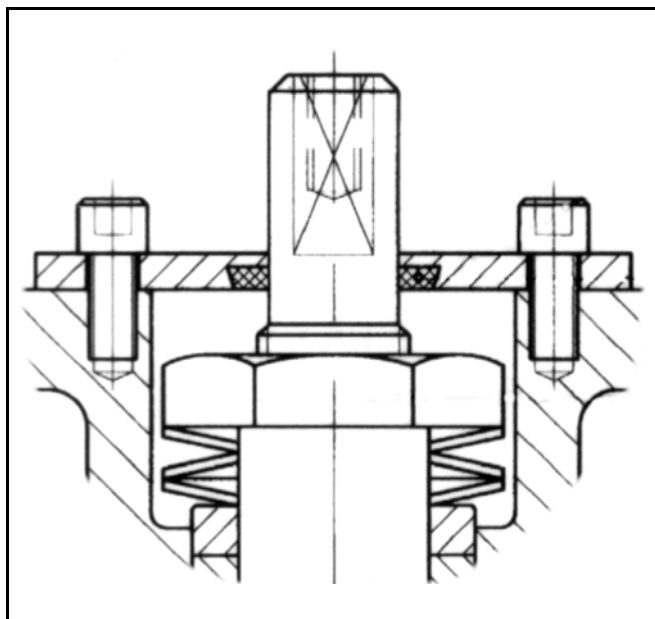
• Уплотнительное кольцо, прижимаемое тарельчатыми пружинами
